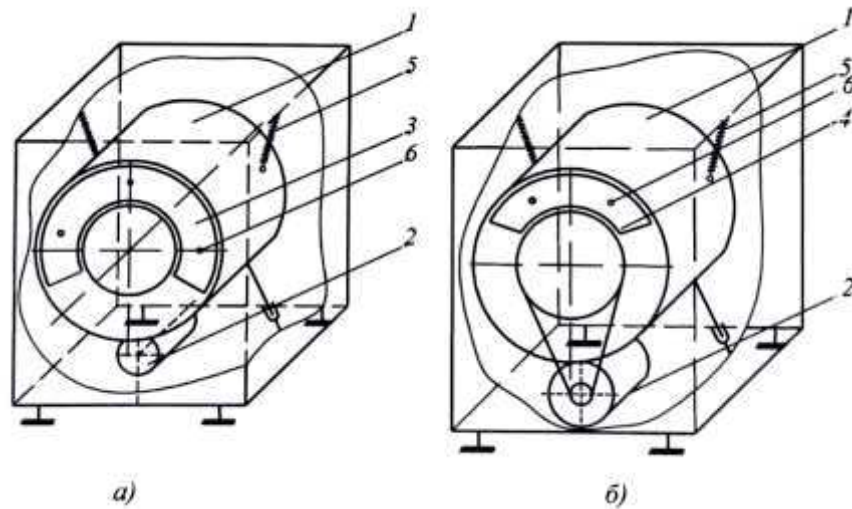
Схема розташування противаг: 1 - бак; 2 - електродвигун; 3, 4 - противаги; 5 — пружини; 6- болти
